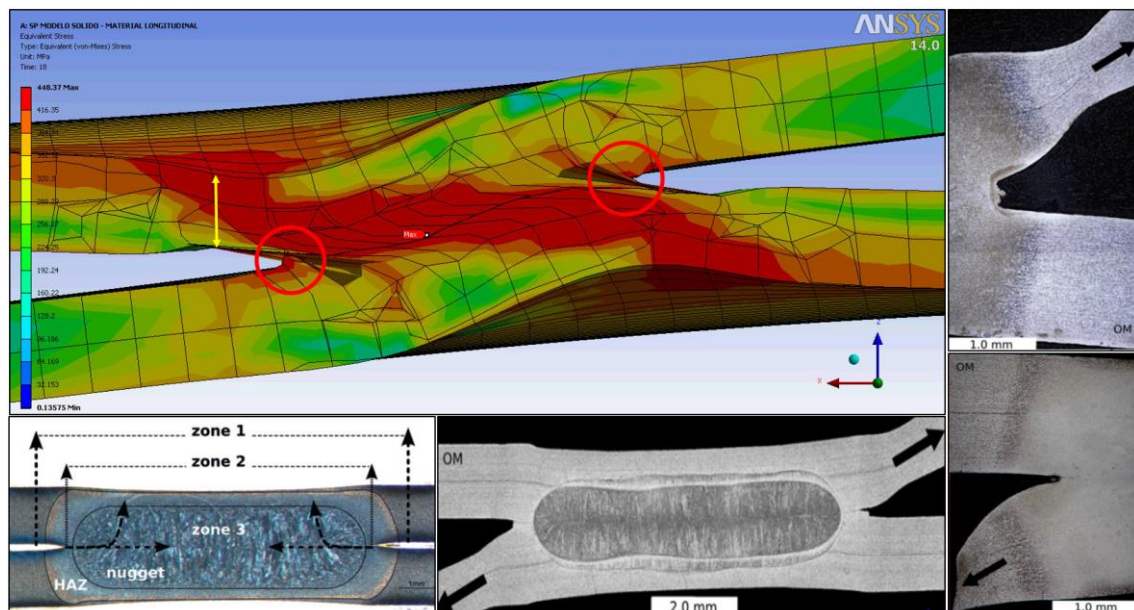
Tensiones de Von Mises [MPa]. Vista en planta y secciones en detalle de la zona central.
